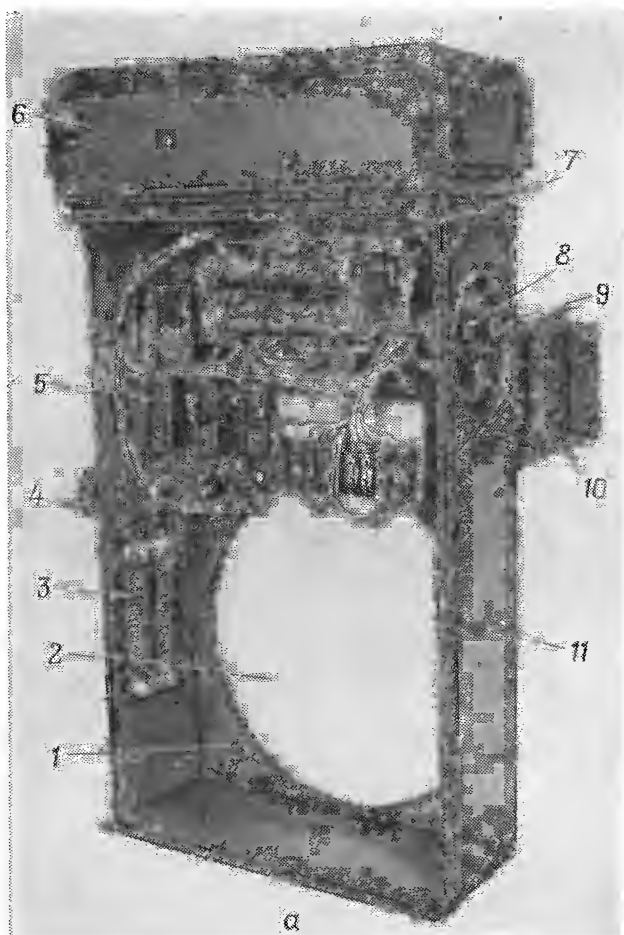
Подшипниковые щиты генератора ГАБ-8-0/230/Ч-425:
